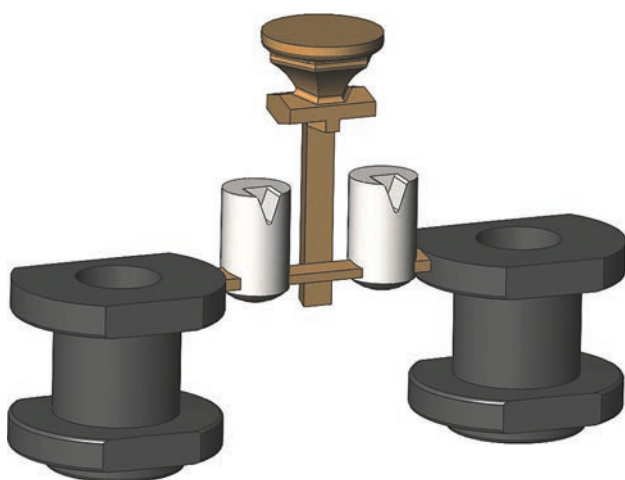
Отливки «Корпус» с литниково-питающей системой
